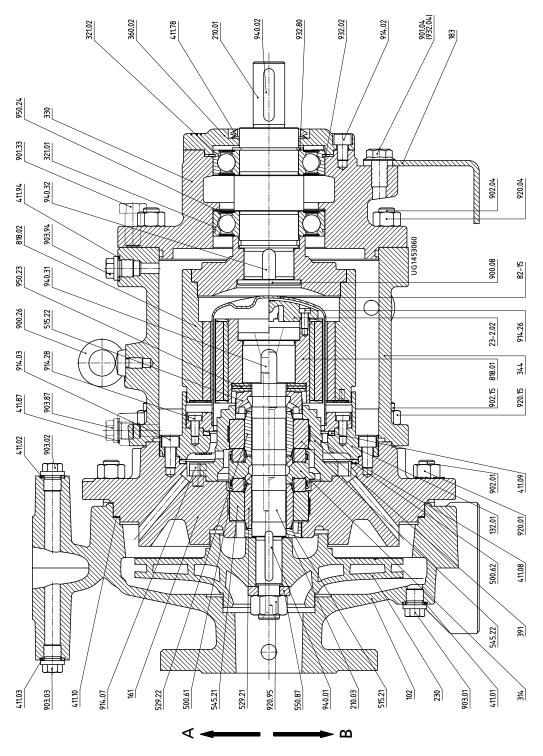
Gesamtzeichnung Ausführung mit geschraubtem Deckel mit Zwischenstück
